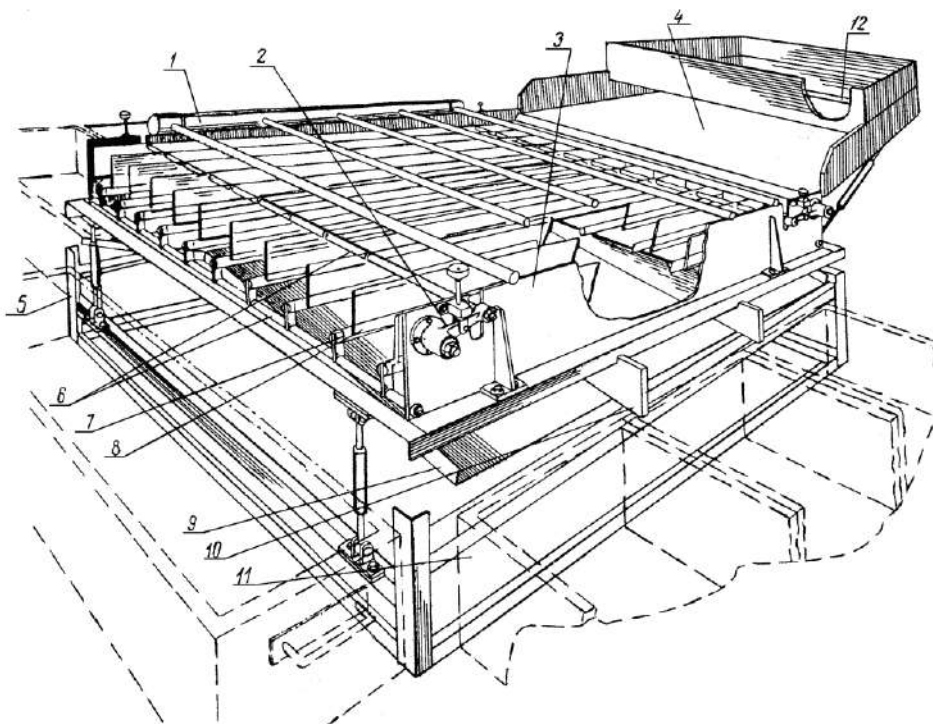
Установка для сортировки живой рыбы конструкции Гидрорыбпроект
